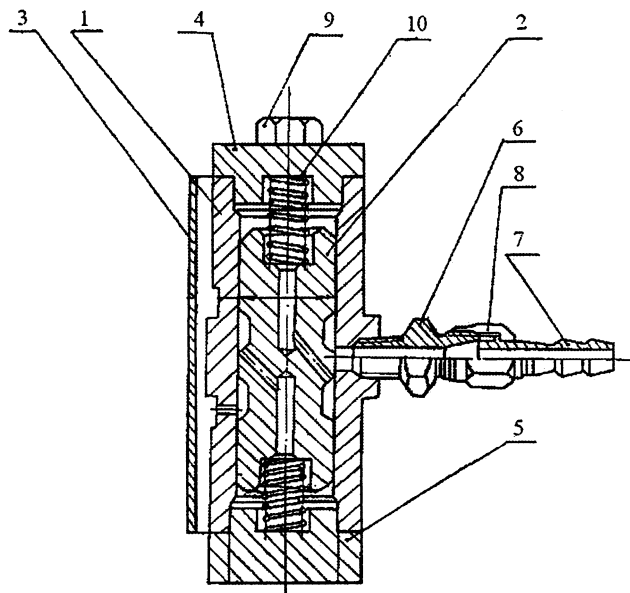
Схема пневматического вибратора: 1 – корпус; 2 – золотник; 3 – кожух; 4 – фланец верхний; 5 – фланец нижний; 6 – штуцер; 7 – ниппель; 8 – гайка; 9 – болт; 10 – пружина
